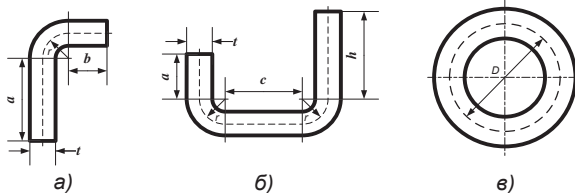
Схема для определения длины заготовок с внутренними закруглениями: а) угольника, б) скобы, в) кольца
